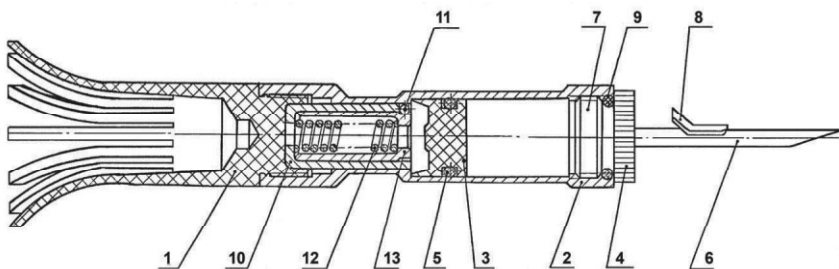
Летающий шприц ШЛ-28: 1 – стабилизатор; 2 – корпус; 3 – поршень; 4 – узел инъекционной иглы; 5 – резиновое кольцо; 6 – игла; 7 – втулка; 8 – зацеп; 9 – резиновое кольцо; 10 – втулка; 11 – шарик; 12 – пружина; 13 – стакан.
